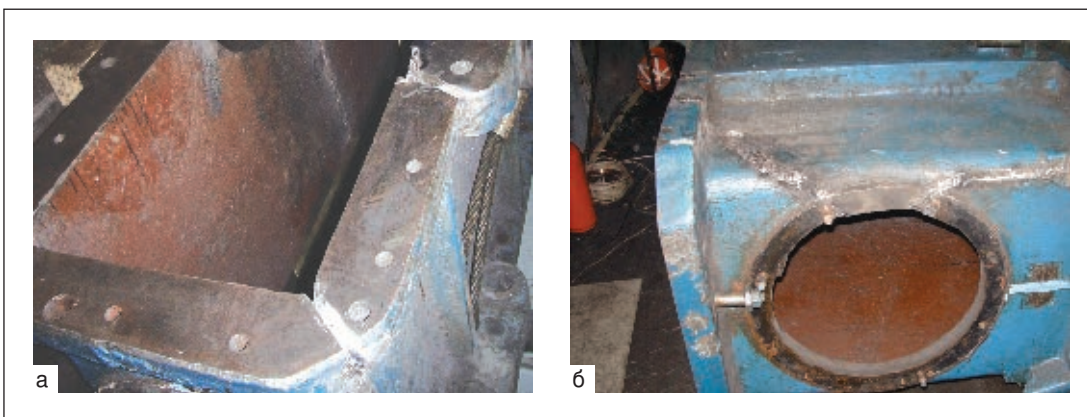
Внешний вид корпуса (а) и сварных швов (б)
